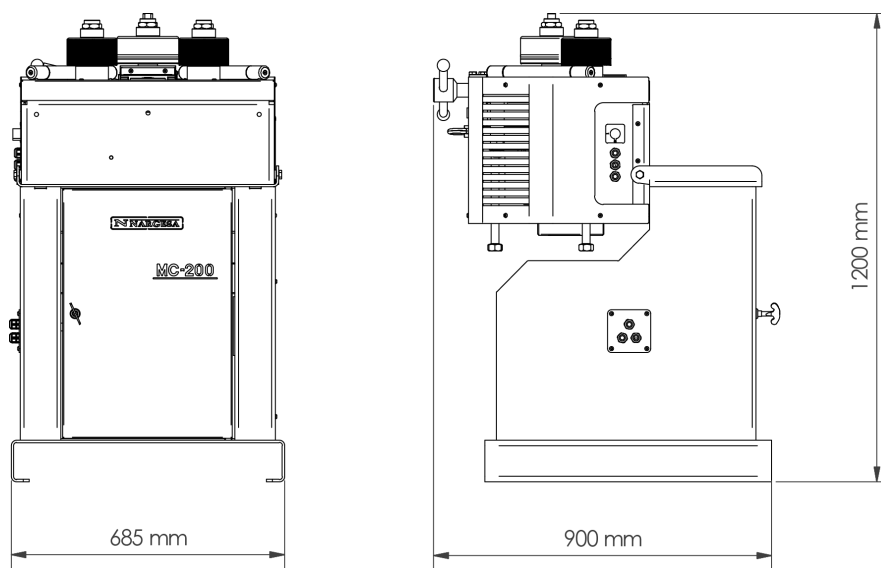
Dimensions de la machine avec le bâti en position horizontale
